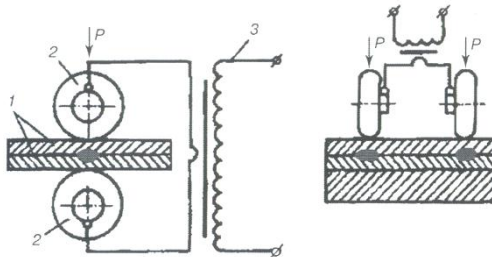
Схема шовной сварки: 1 - свариваемые заготовки; 2 - медные ролики (электроды); 3 - сварочный трансформатор
